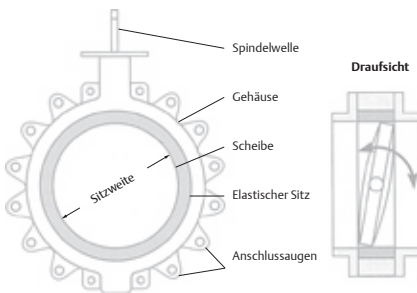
Drosselklappe in Flanschaugenausführung
